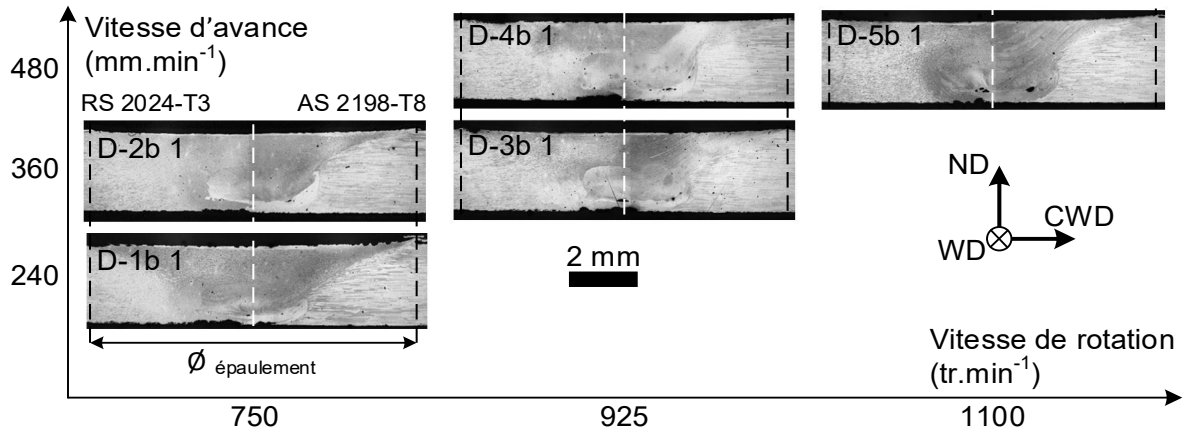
Corrosion des éprouvettes brutes vues dans la section transverse (CWD-ND).
